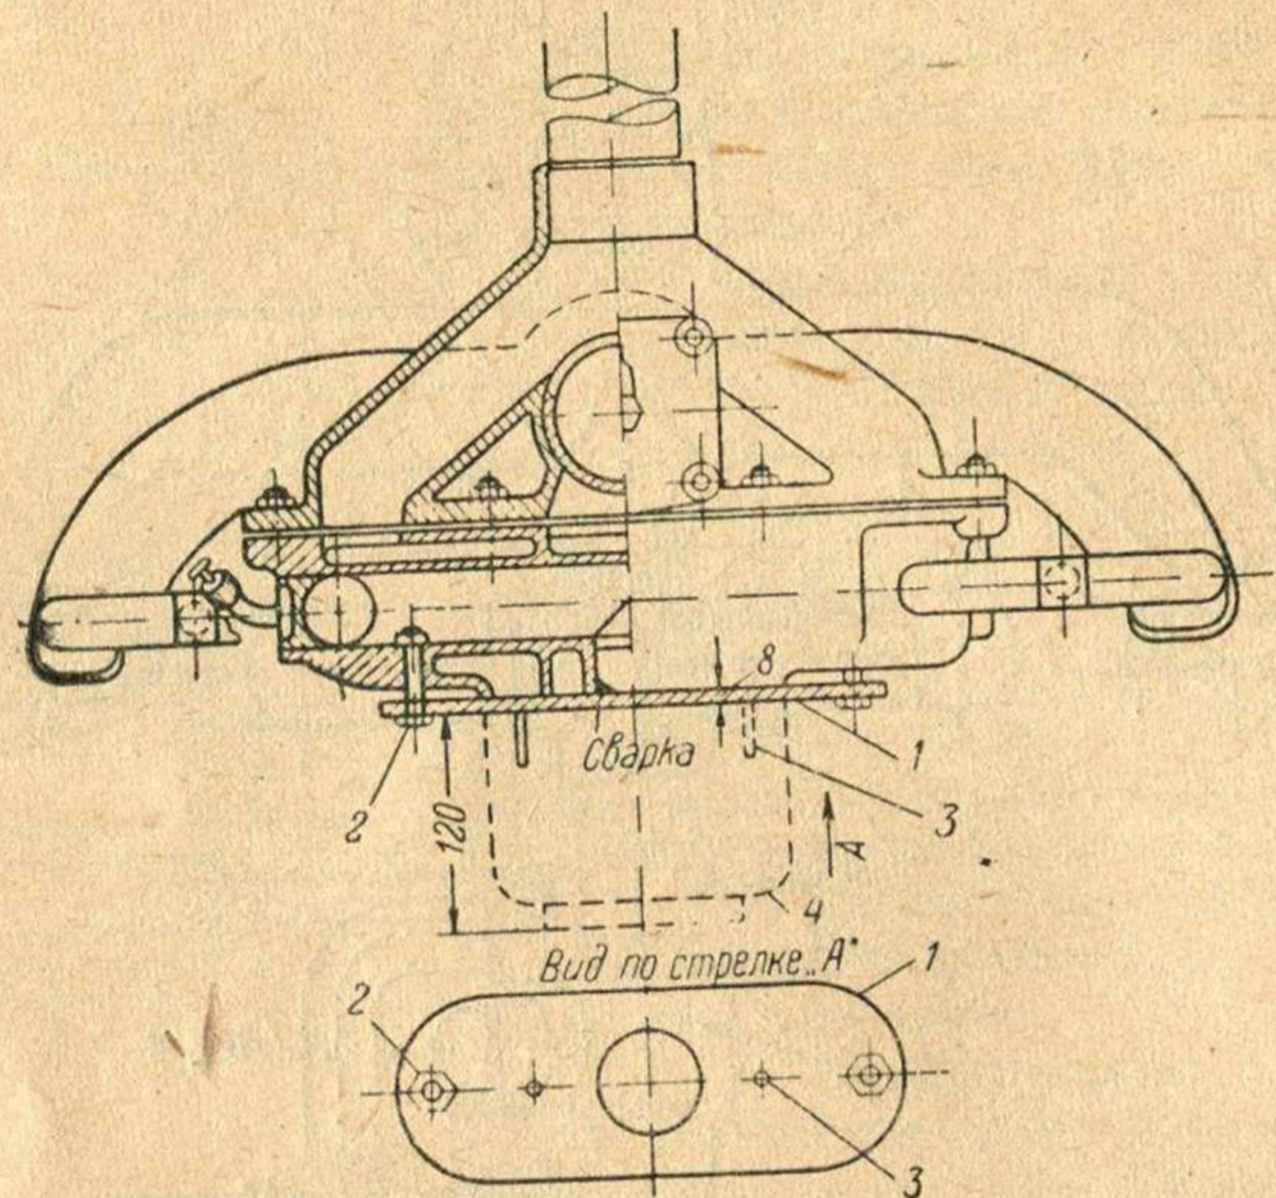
Жидкотопливный коллектор СХТЗ-НАТИ, приспособленный для работы на газе:
